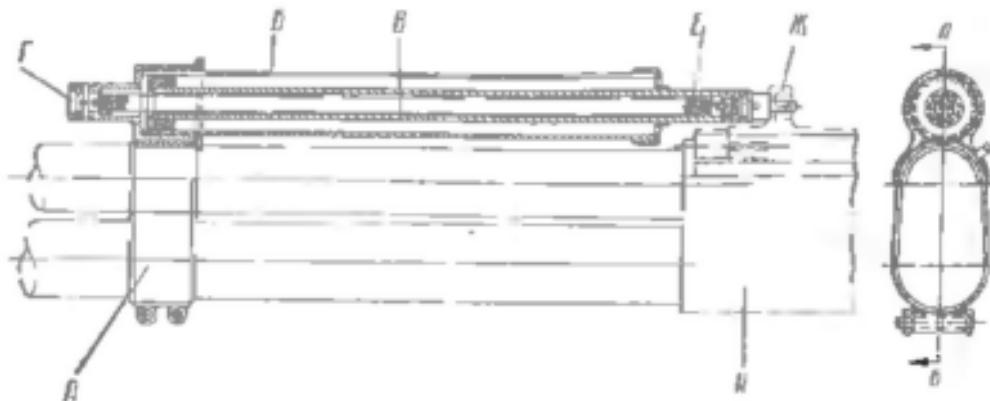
Цилиндр пневмоперезарядки пулемета БС.
